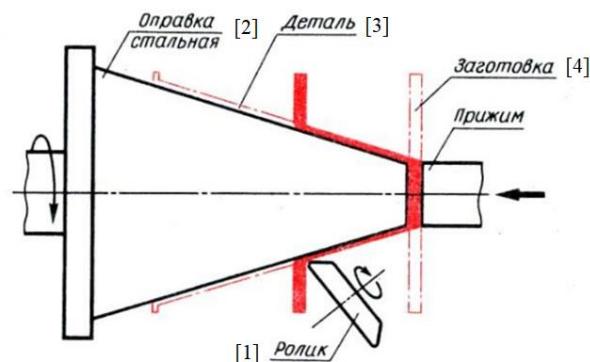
Сущность процесса ротационной вытяжки. 1 — обжимной ролик; 2 — вращающаяся оправка; 3 — получаемая деталь; 4 — плоская заготовка;
